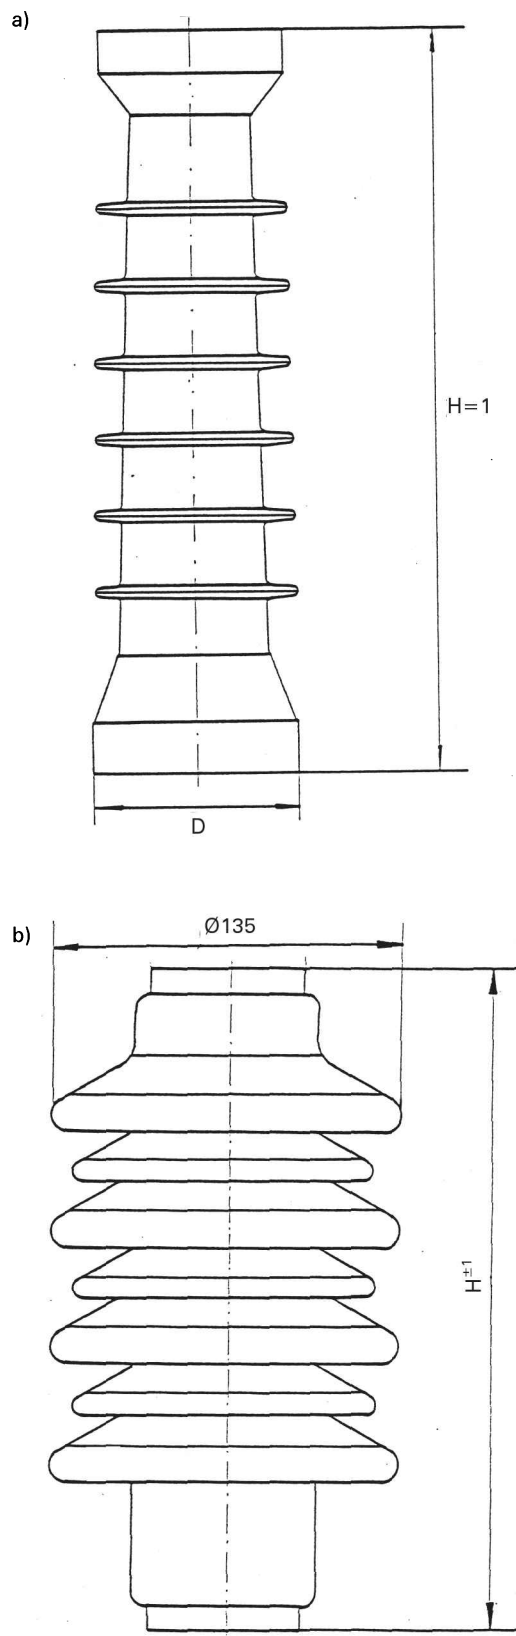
Aisladores. a) De interior. b) Para exteriores.
